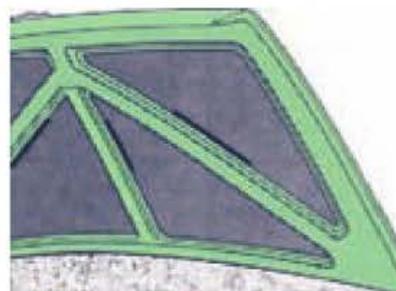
Aplicación de la cinta adhesiva de espuma negra.
